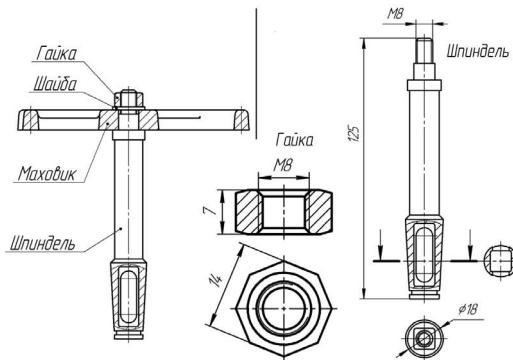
Изображения сборки и двух её деталей для задания в номинации № 3
